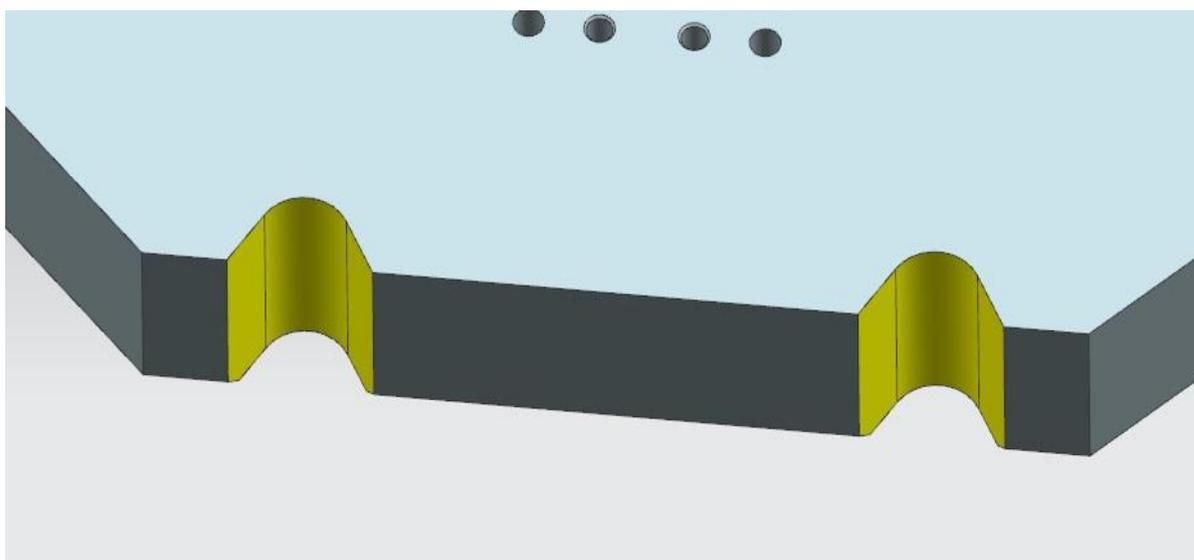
Освобождения для быстрой установки штампа на пресс
